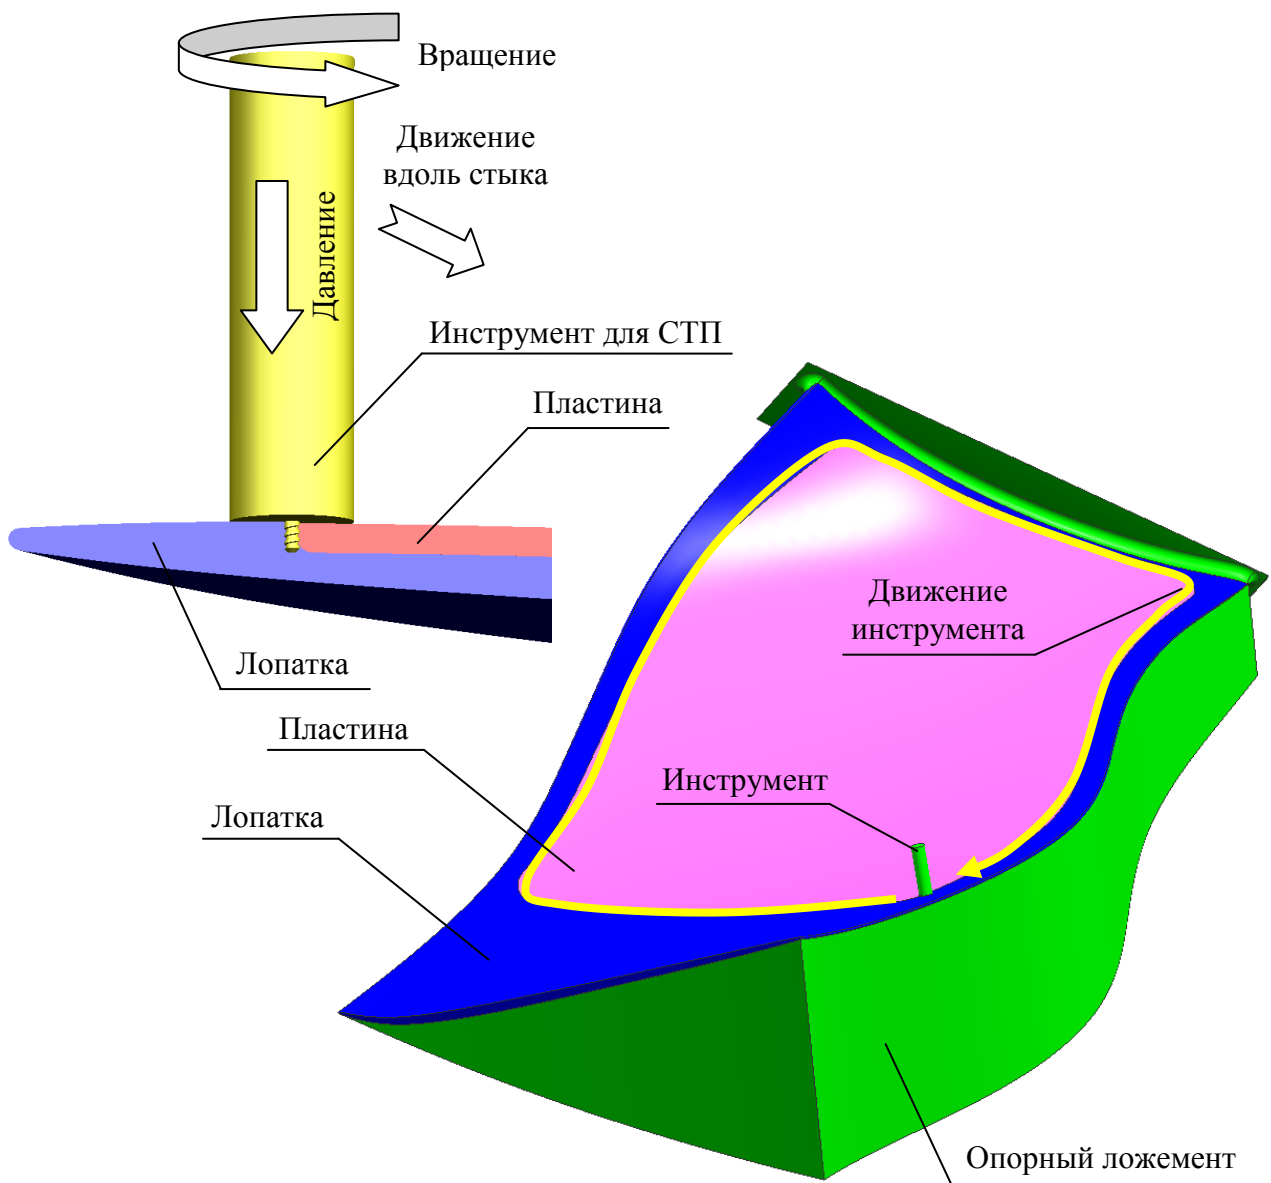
Процесс сварки трением с перемешиванием
